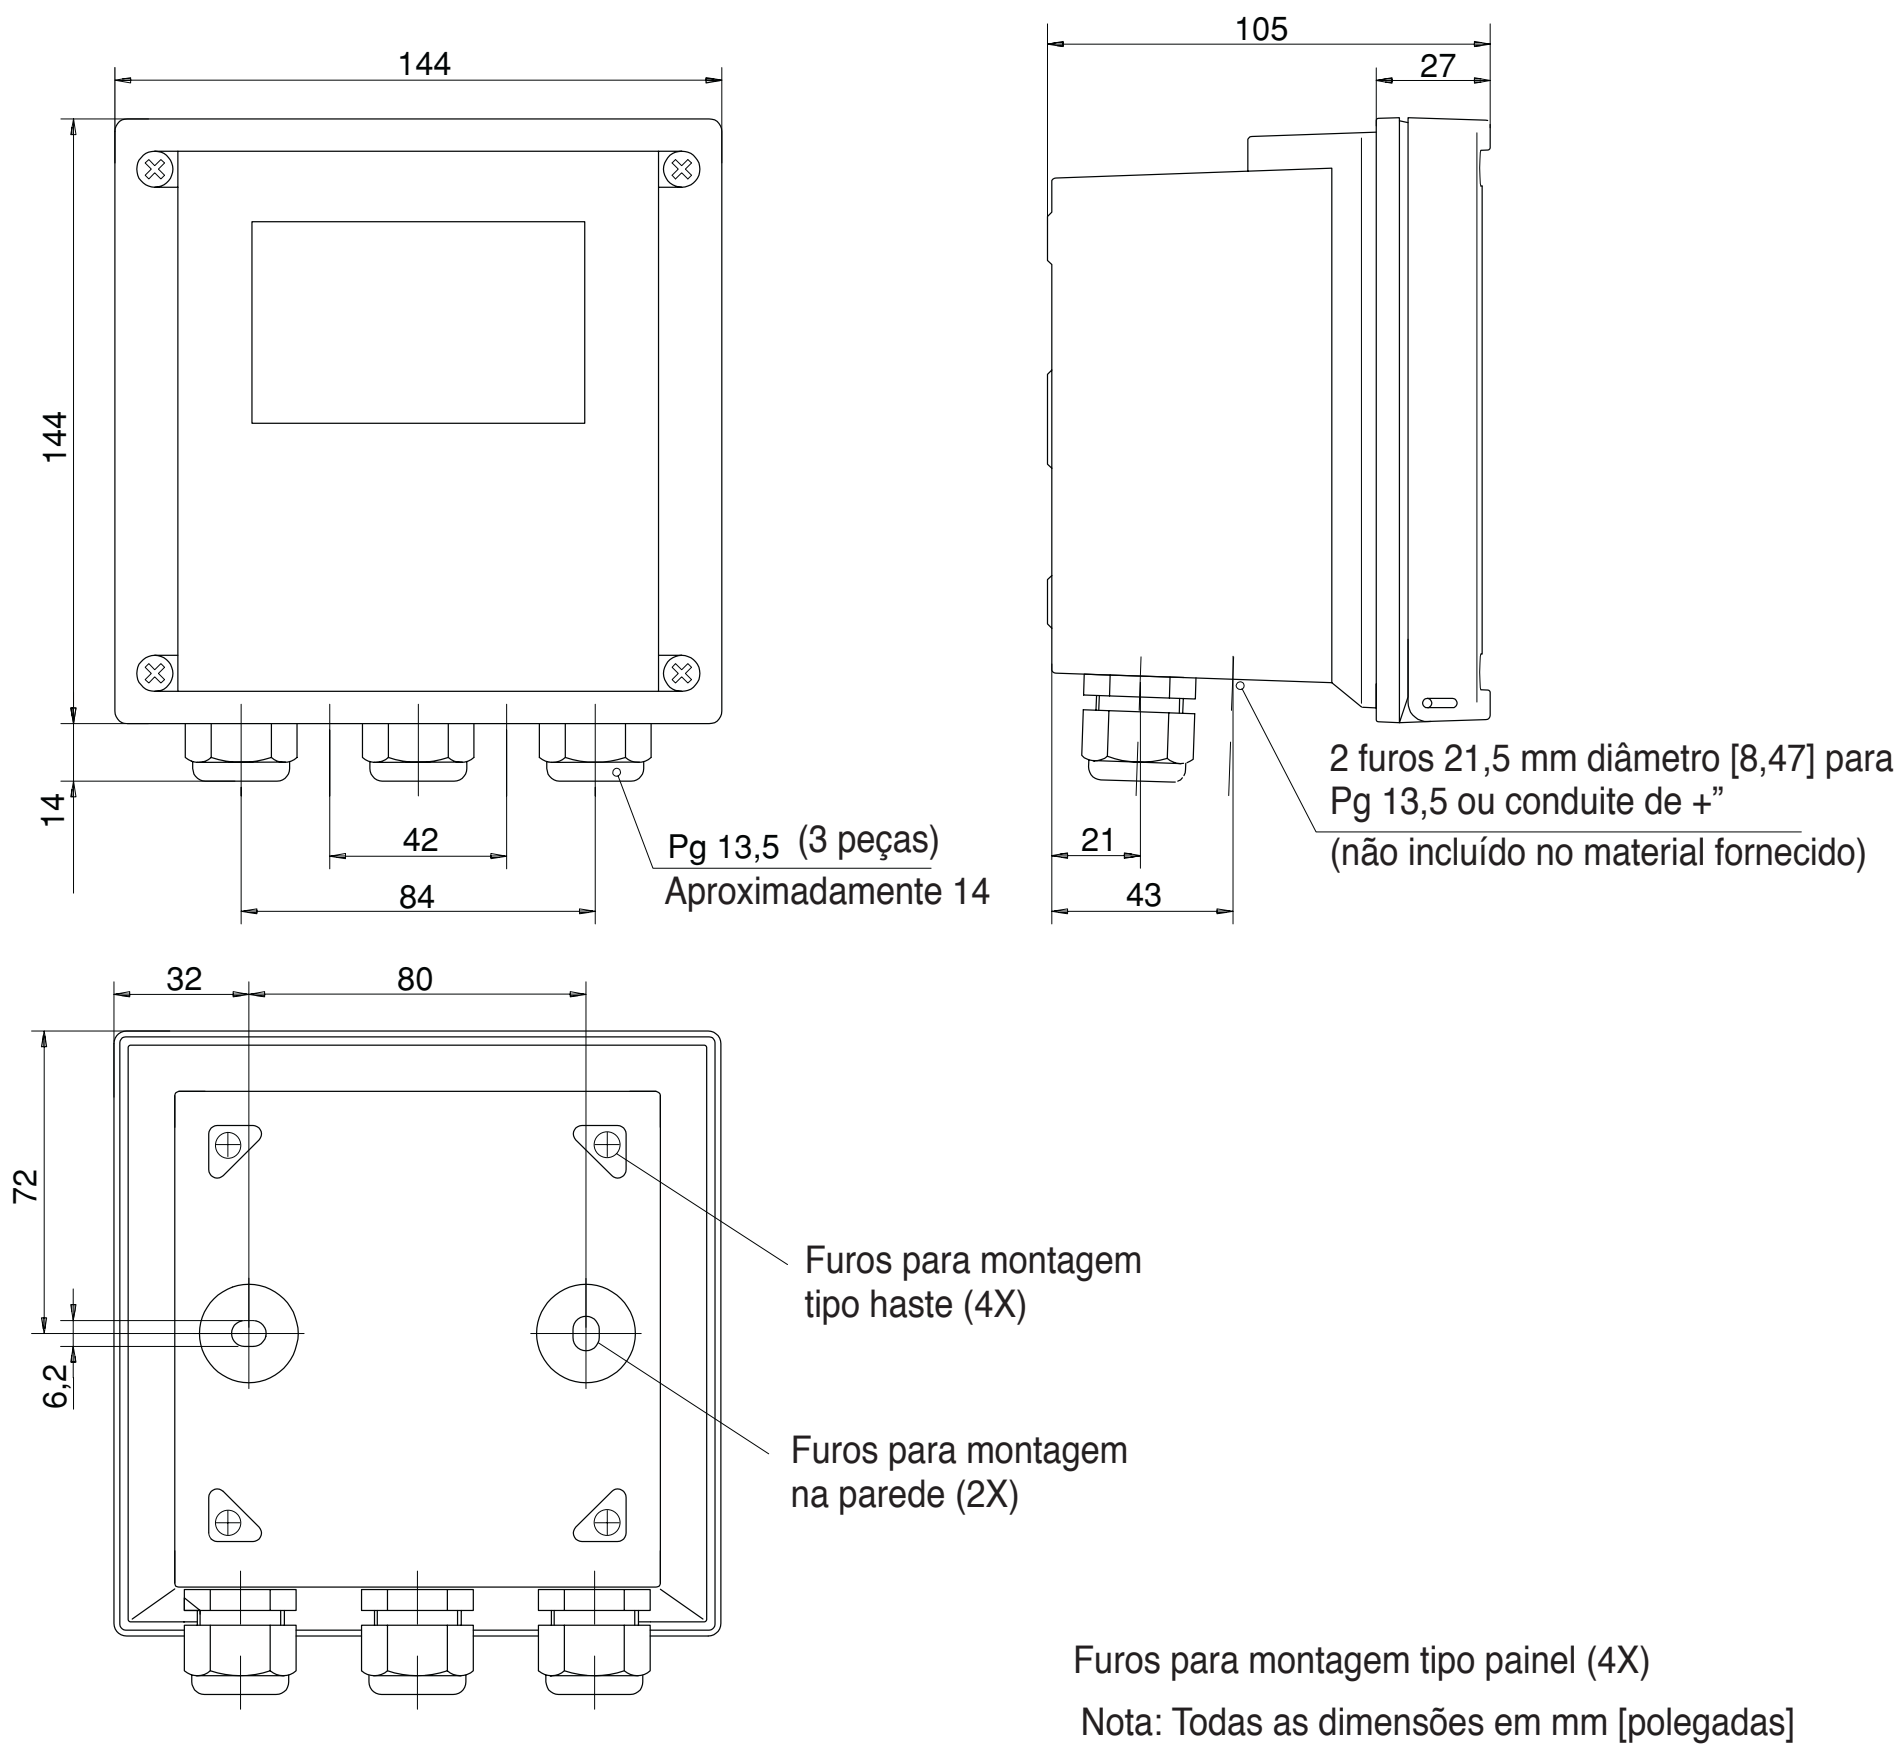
Desenho das dimensões do Transmissor e diagrama de montagem
